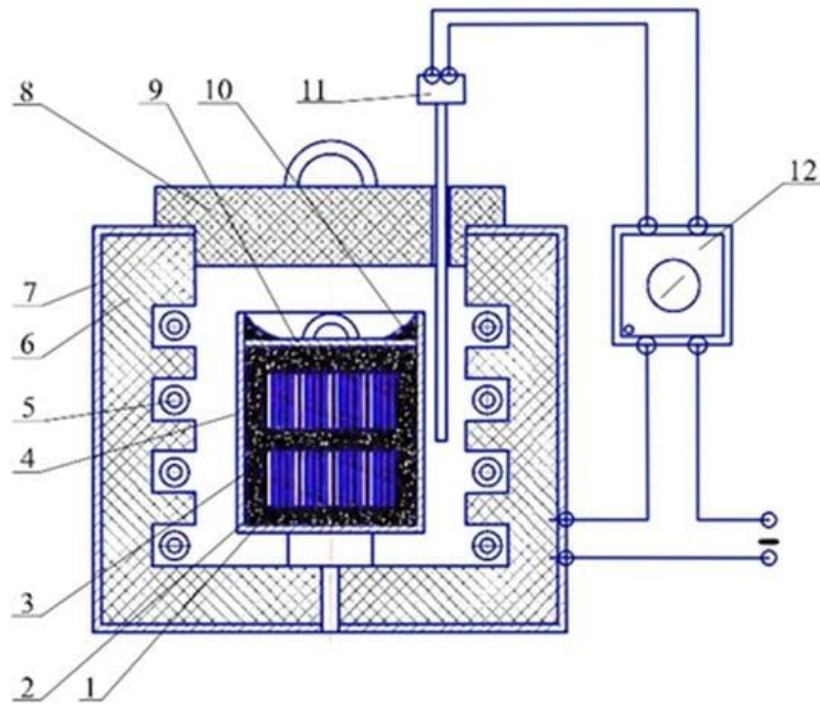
1.2 - Конструктивна схема стану для нітроцементування арматурних тарілок: 1—пластина; 2—вуглецево-азотне покриття; 3—наповнювач (пісок з технічним вуглецем); 4—контейнер; 5—електронагрівач; 6—футеровка печі; 7—корпус топки; 8—кришка топки; 9—кришка контейнера; 10—піщано-глиниста плomba; 11—термопара; 12—регулятор температури
